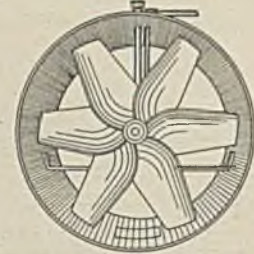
Schraubenventilator von Korfmann mit sechs breiten Flügeln.
